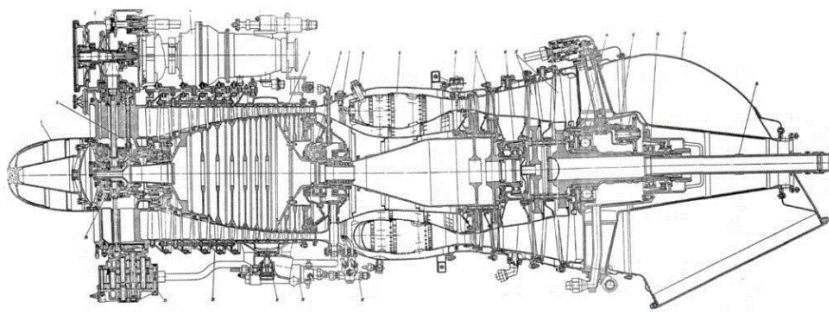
Вертолетный двигатель ТВЗ-117
